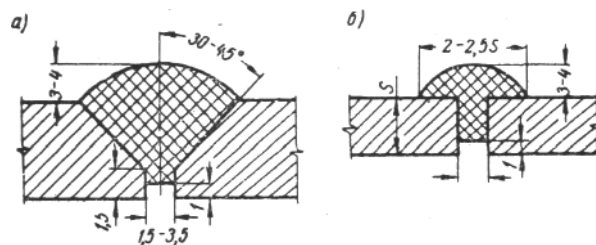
Типи зварних з'єднань сталевих труб:
